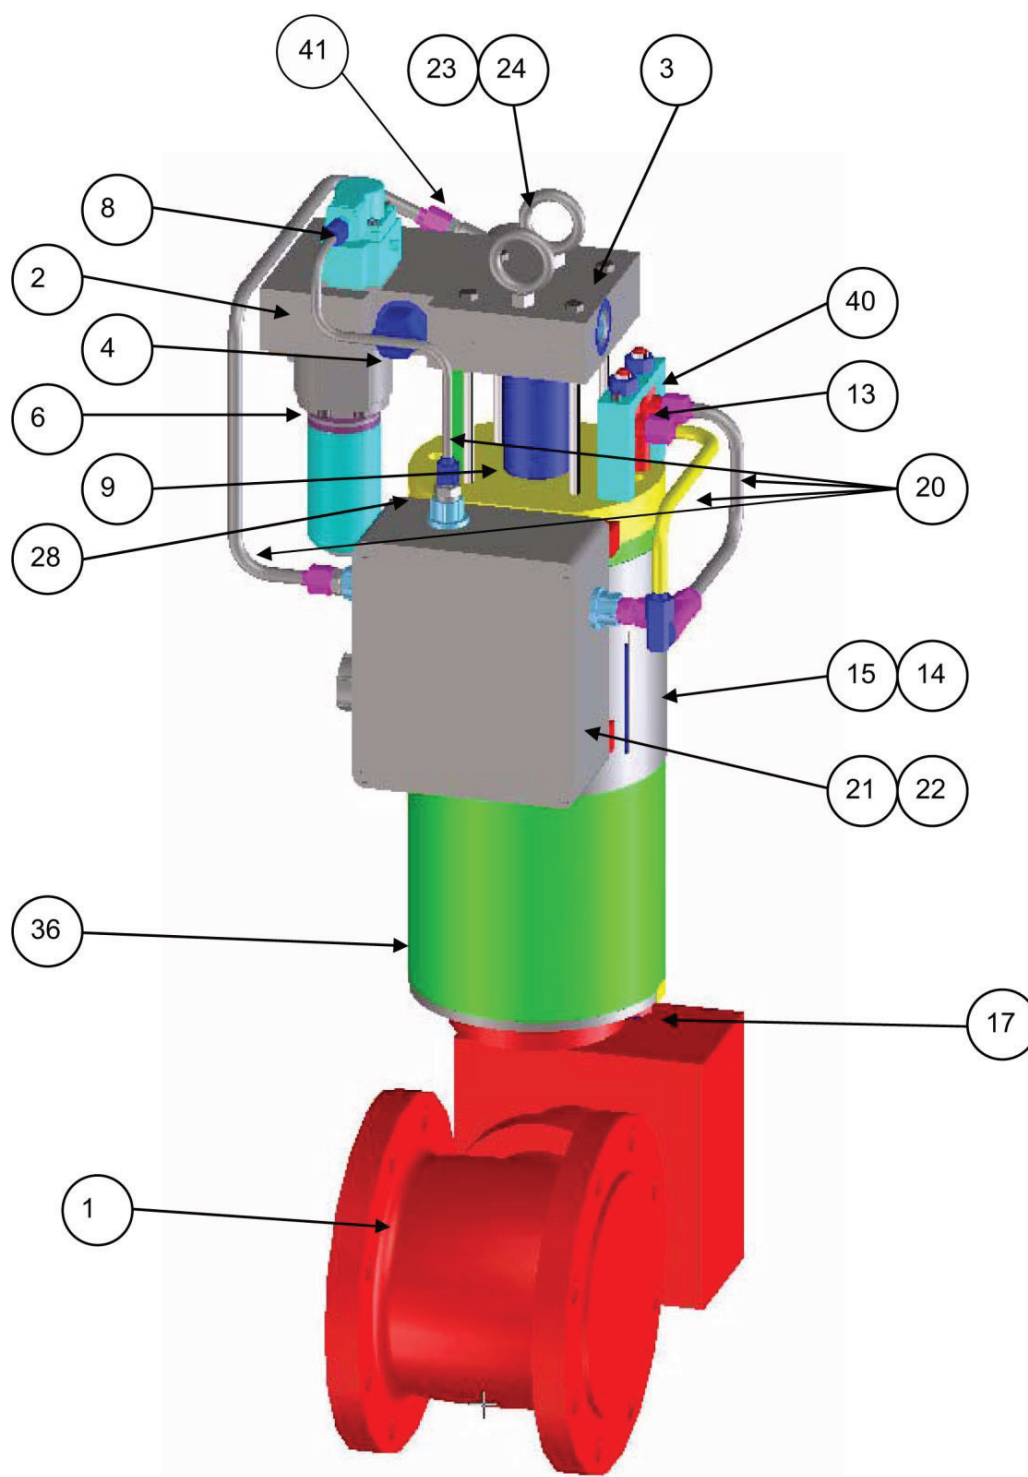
а. Запорно-регулирующий газовый клапан (Общее устройство)
